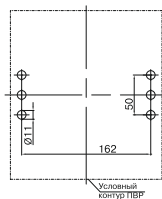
Габаритные и установочные размеры ПВР-160, ПВР-250, ПВР-400, ПВР-630
